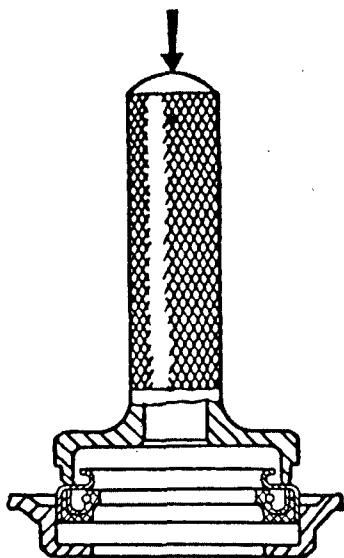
Запрессовка манжеты в крышку распределительных шестерен оправкой 5-У-27733
